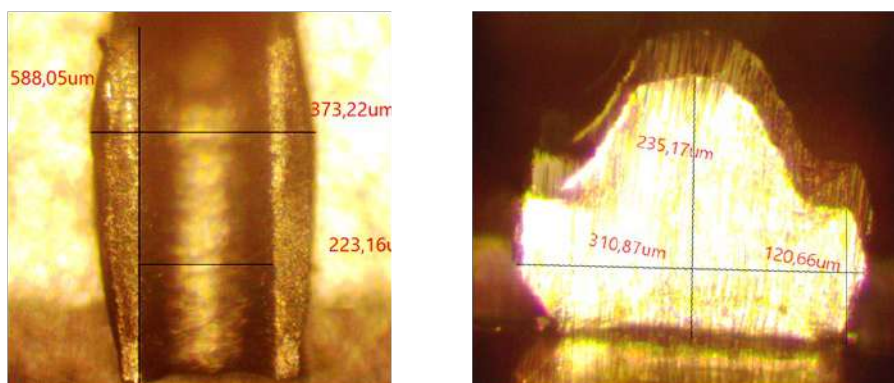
Форма и размеры сварного соединения в двух проекциях при времени сварки 120 мс.
